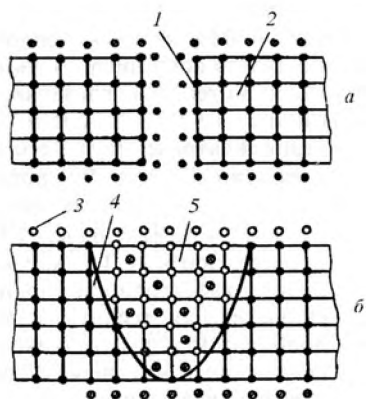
Схема образования соединения при сварке плавлением
